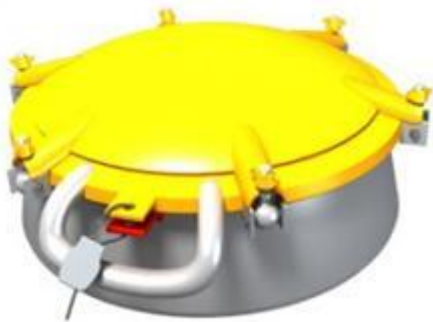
Схема установки универсального ЗПУ с длиной каната 300 мм на верхней крышке загрузочного люка цистерны барашкового типа со специальными пломбировочными проушинами
